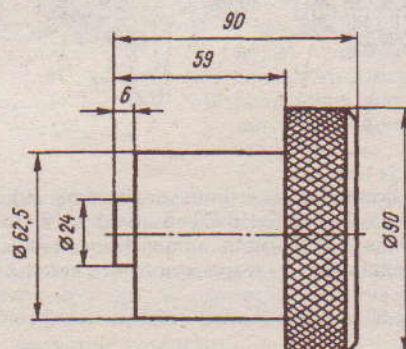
Оправка для запрессовки приводного вала в средний подшипник и зубчатого хвостовика с подшипником в сборе в кожух
